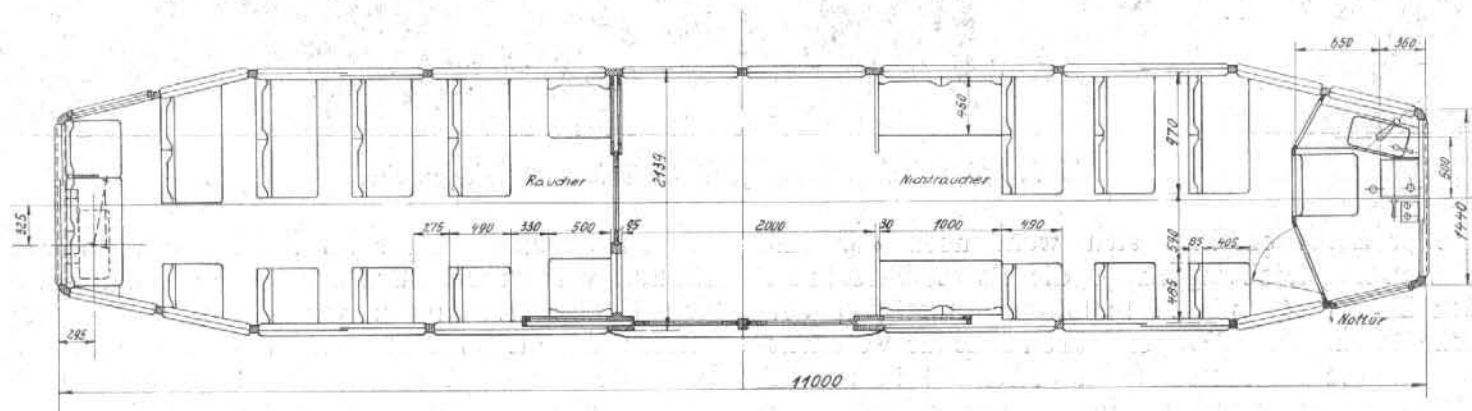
Einrichtungstriebwagen. Grundriss.
